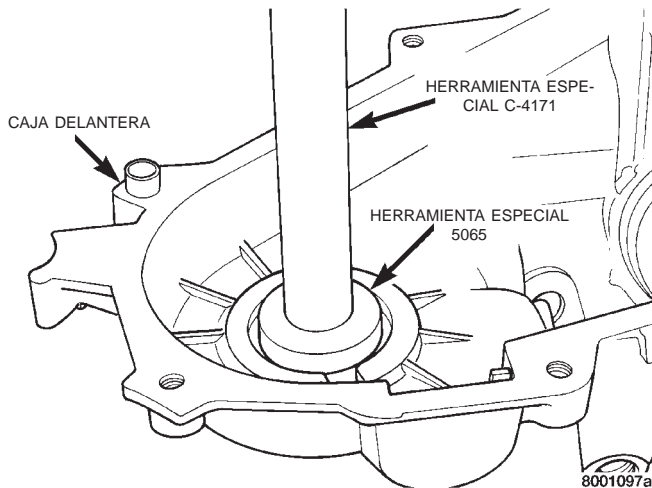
Desmontaje de cojinete del eje transmisor delantero
